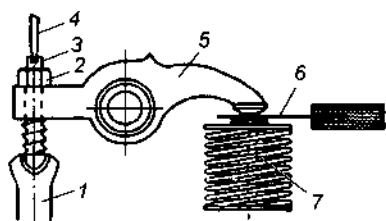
Регулировка теплового зазора в ГРМ с нижним расположением распределительного вала: 1 — штанга; 2 — контргайка; 3 — регулировочный винт; 4 — отвертка; 5 — коромысло; 6 — щуп; 7 — клапан
